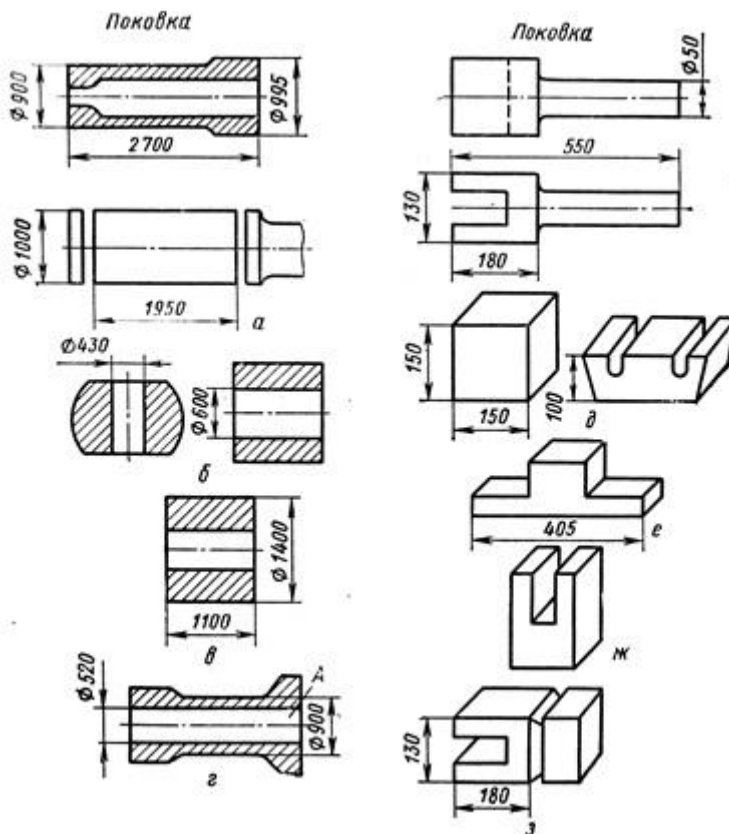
Последовательность операцийковки пологод цилиндра и рычага с вилкой
